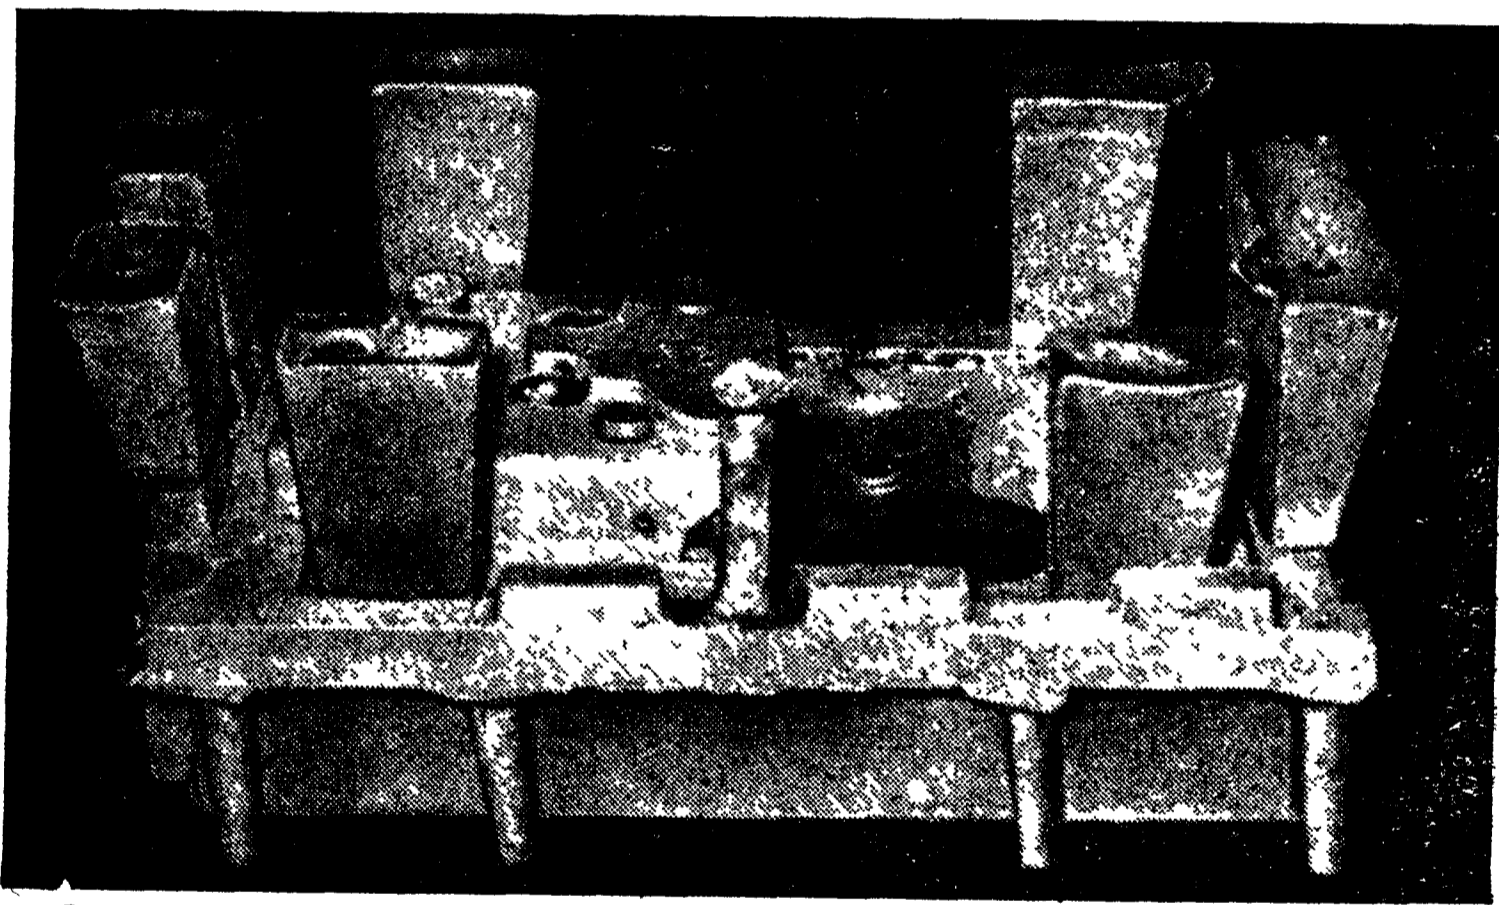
Корпус из сплава АЛ2, отлитый с применением улучшенной литниковой системы (масса отливки без прибылей 20 кг, габаритные размеры 750×340×120 мм)
